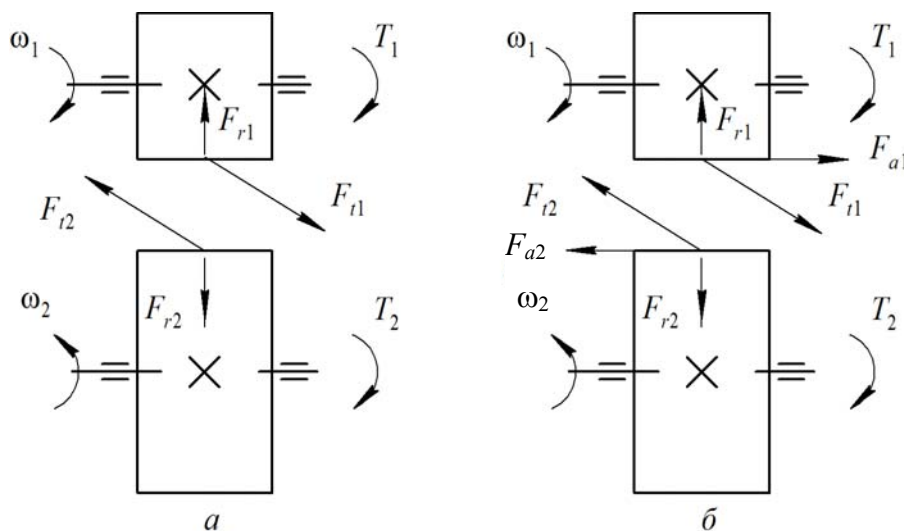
Силы в зацеплении цилиндрических зубчатых колес:
